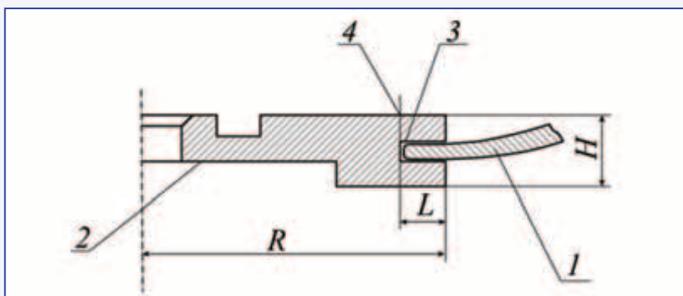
Схема ремонта лопаток компрессора методом электронно-лучевой сварки: 1 - перо лопатки; 2 - вставка; 3 - паз для пера лопатки; 4 - риска для наведения электронного луча на стык
